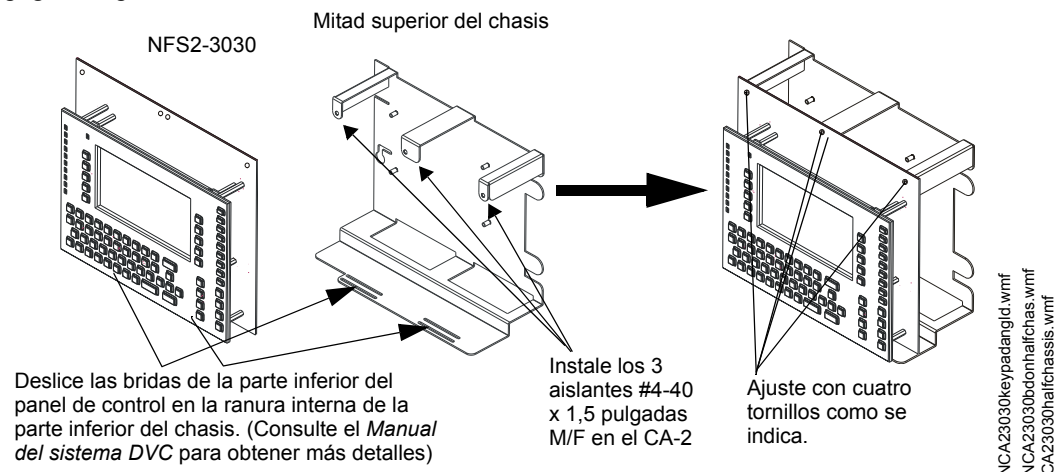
Montaje del NFS2-3030 en la mitad del chasis CA-2
